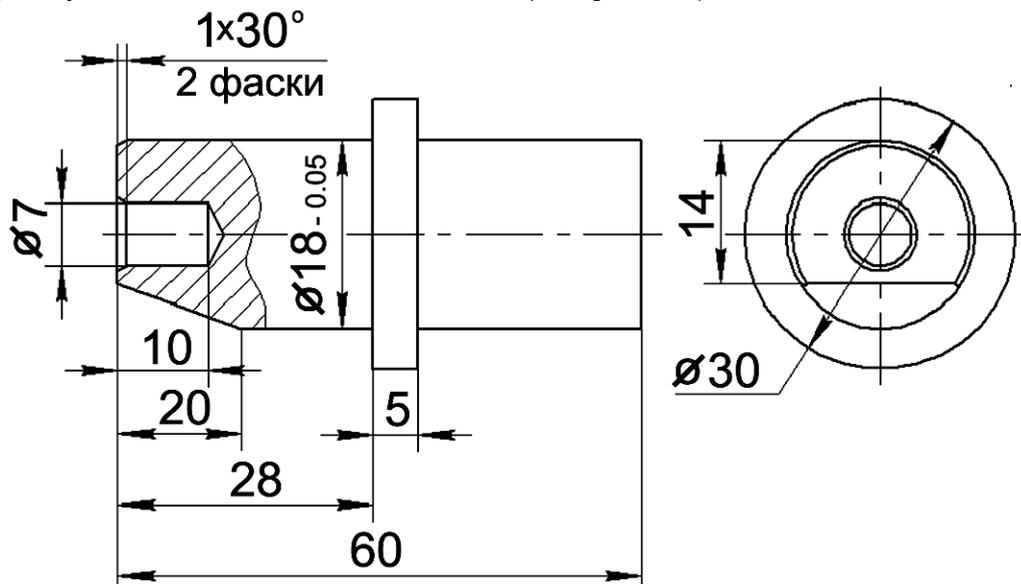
Приспособление для фиксации установочного штифта
